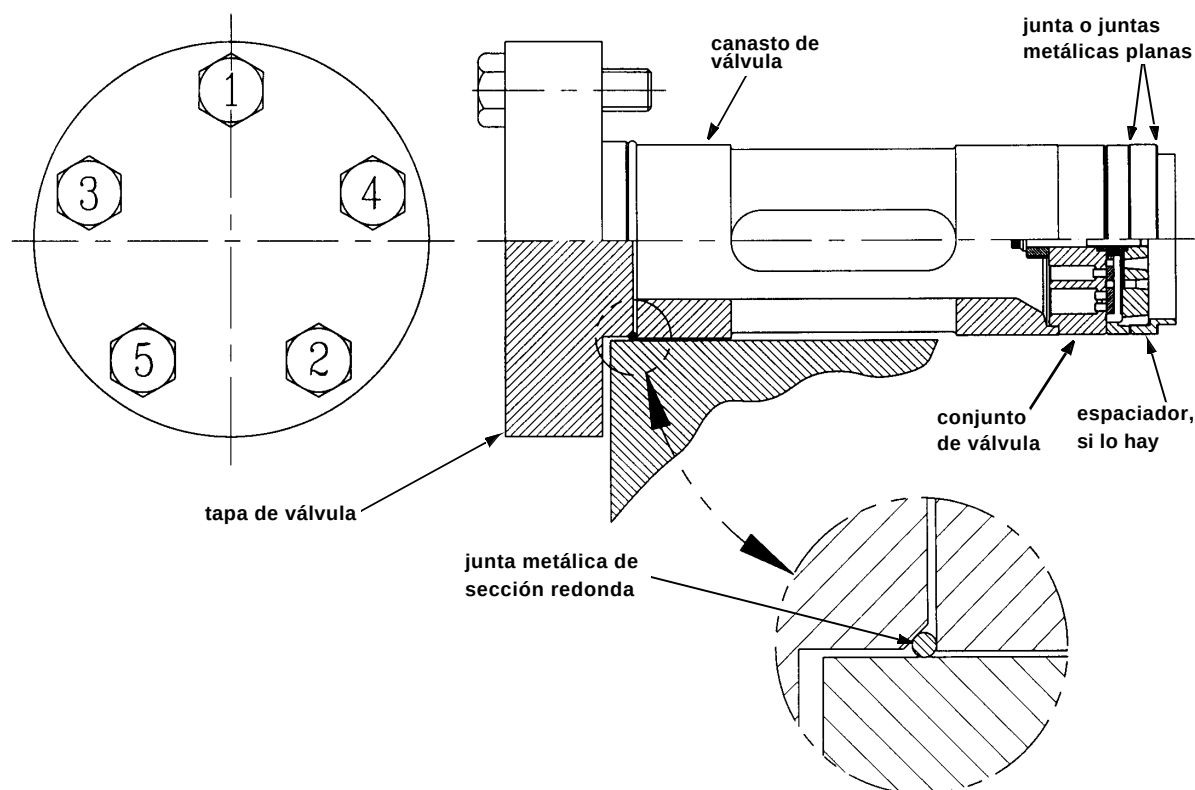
MONTAJE DE TAPA DE VÁLVULA DE ALTA PRESIÓN
